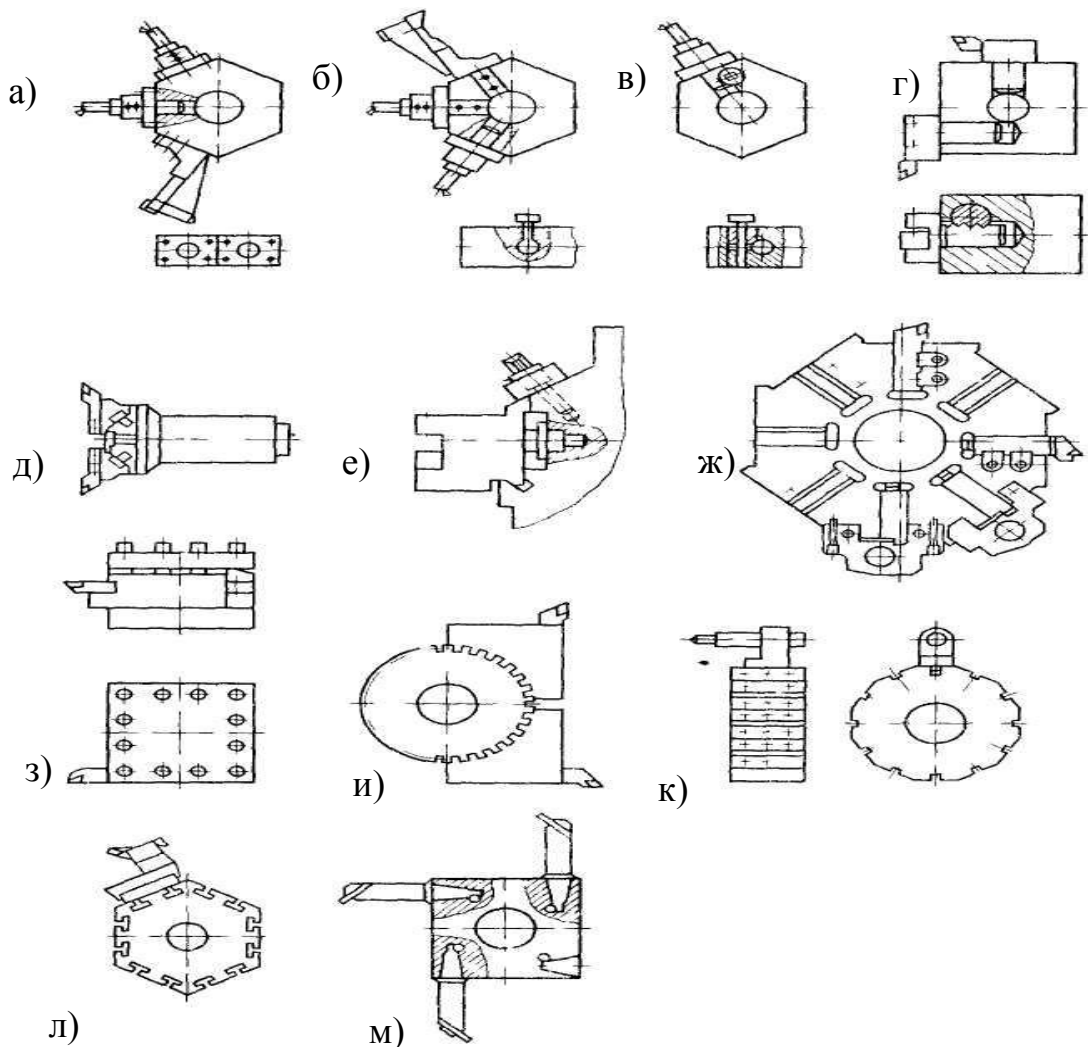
Основные схемы способов крепления инструмента на токарных станках с ЧПУ
